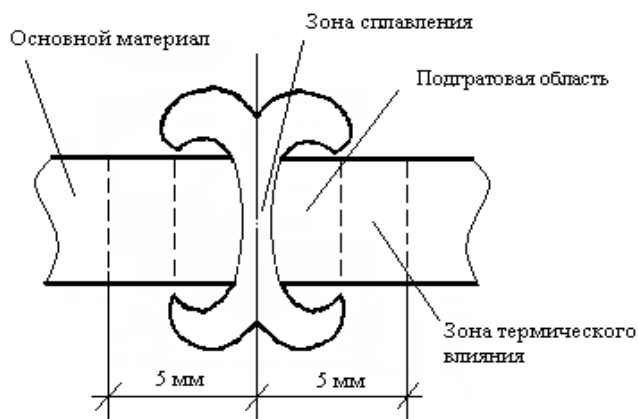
Схема разделения на зоны сварного стыкового соединения ПЭ труб
